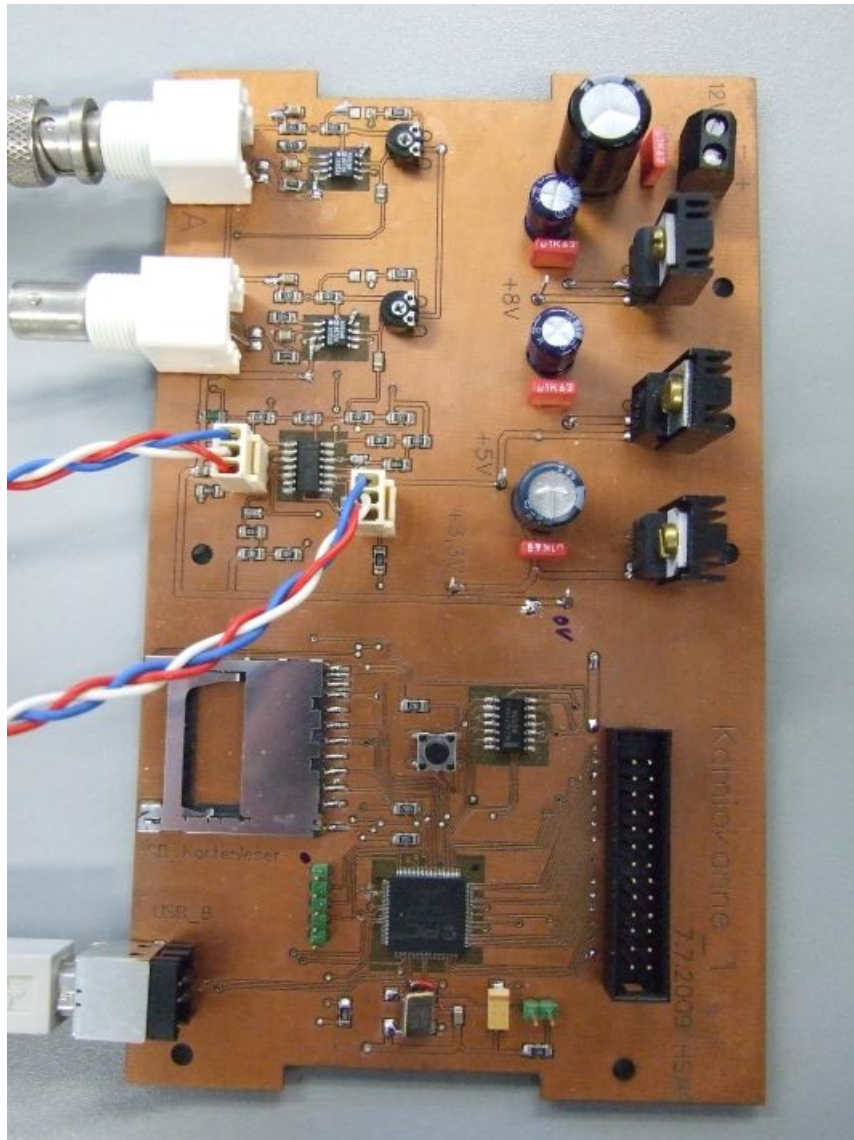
Bestückter gefräster Prototyp der Hauptplatine.
